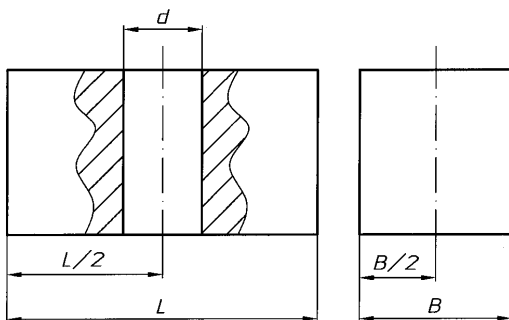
Обозначения размеров заготовки и обрабатываемого отверстия
